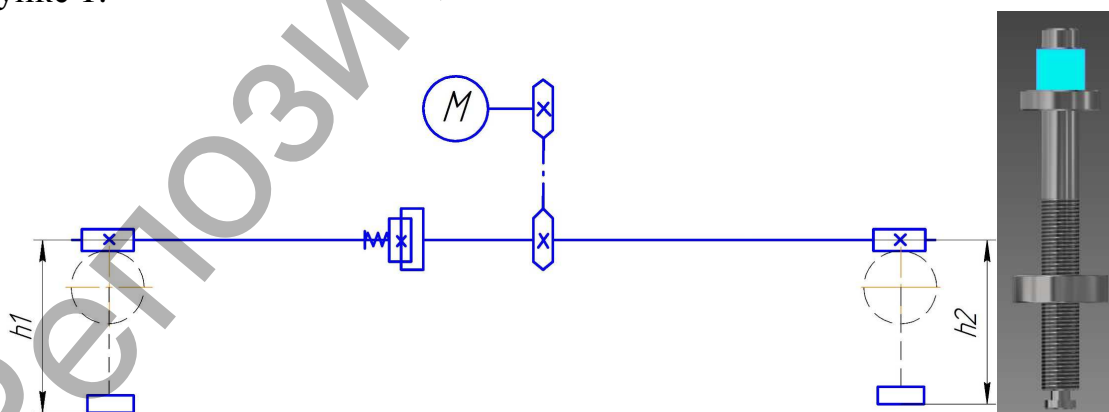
Упрощенная кинематическая схема настройки и поверхность закрепления вала
